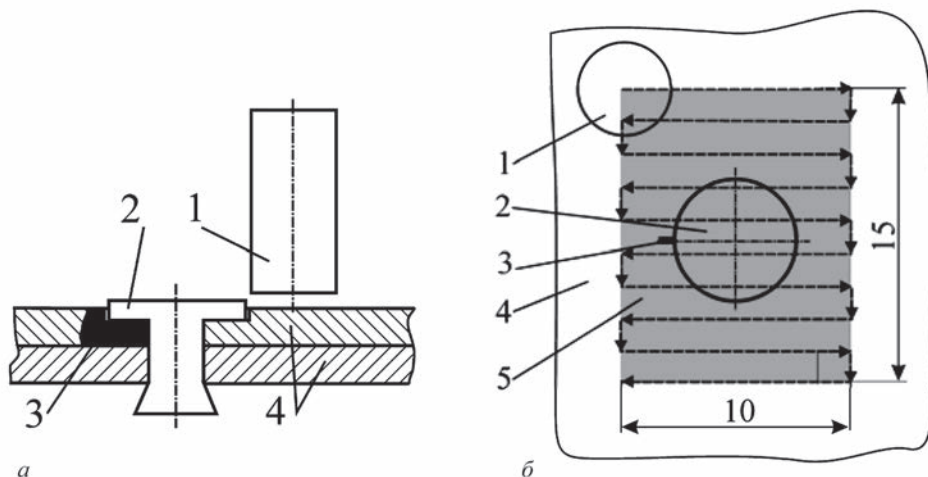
Схема сканування зони заклепок: 1 – ВСП; 2 – заклепка; 3 – дефект; 4 – двохшарова конструкція; 5 – ділянка сканування
